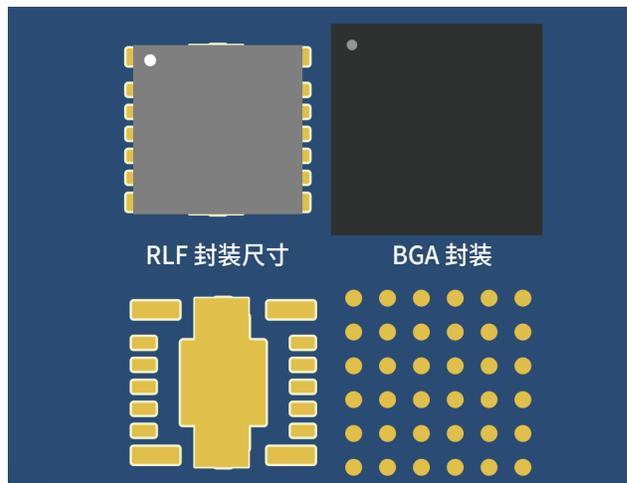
5mm × 5.5mm 增强型 HotRod QFN 封装相较 6.25mm × 6.25mm BGA 封装的热接触面积优势。
